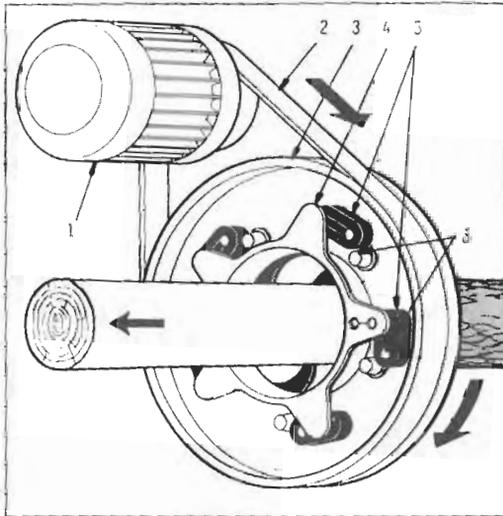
Transmisión y elementos del rotor (CAMBIO). 1.- Motor. 2.- Correa. 3.- Rotor. 4.- Pieza central o "estrella". 5.- Anillos de caucho para tensión. 6.- Extremo de las herramientas.
